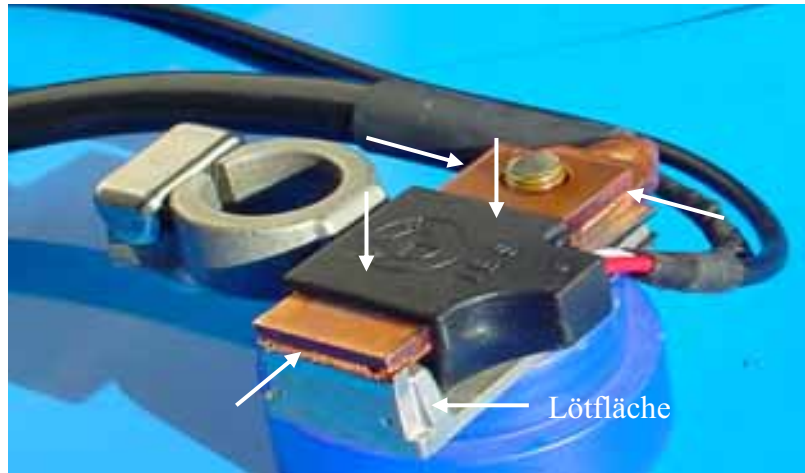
Batteriekabel mit 5 EB-Schweißungen und einer EB-Lötung.
